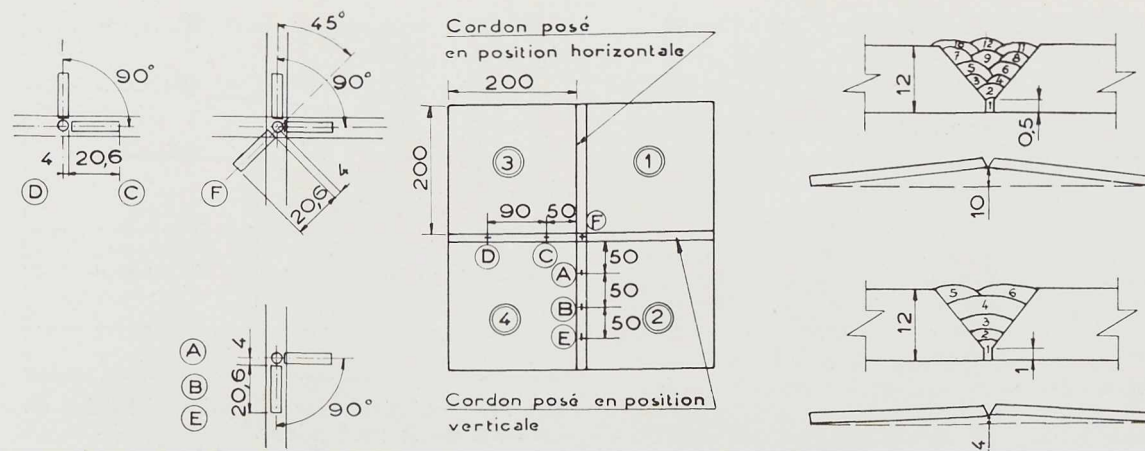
Emplacement des extensomètres ohmiques sur les cordons de soudure assemblant 4 plats.
